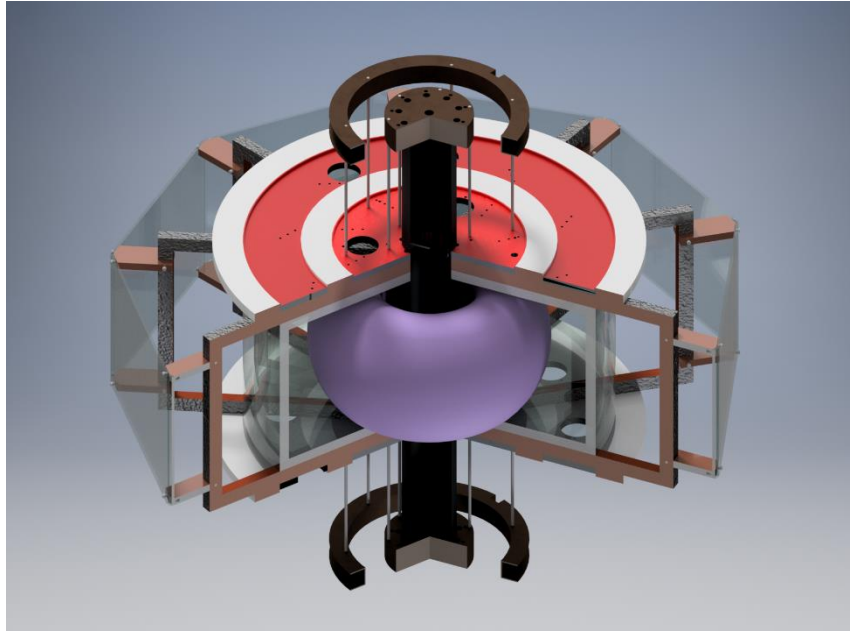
Dibujo CAD del Tokamak Esférico MEDUSA-CR.
